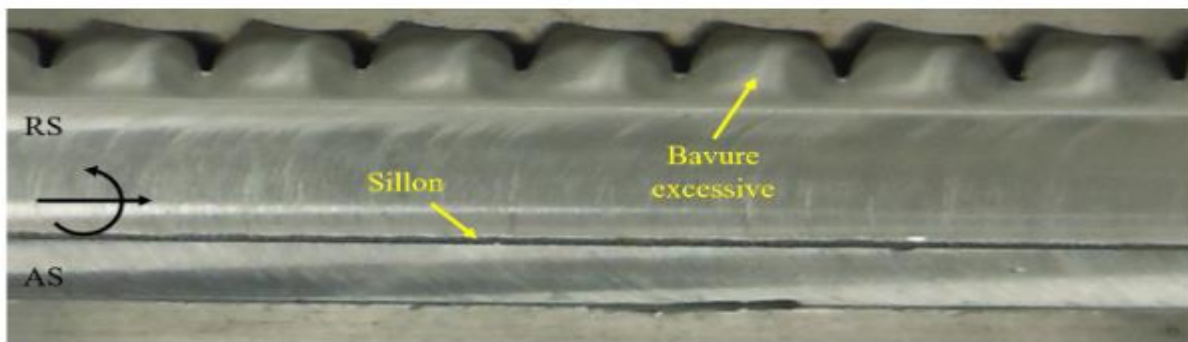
Défauts de surface sur une soudure en 6061-T6 [14]
